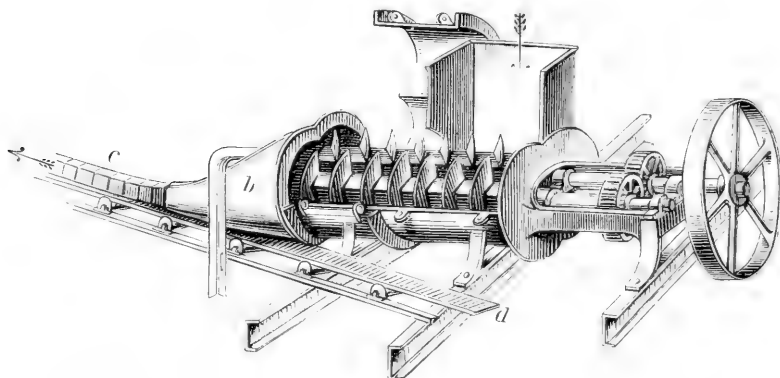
Zerkleinerungszylinder obiger Maschine.
